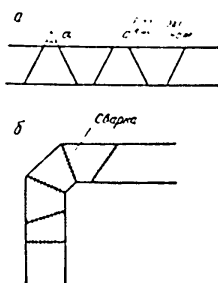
Способ изготовления фланцевых частей из прямых труб
